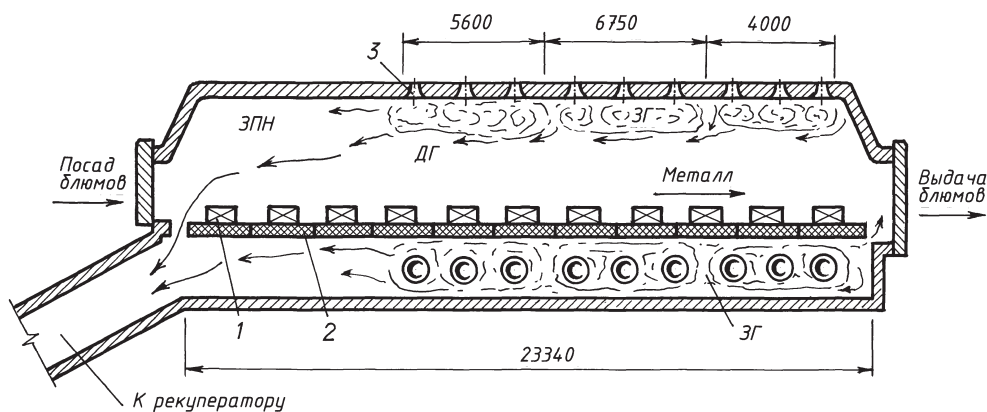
Схема нагревательной печи стана 850 РУП «БМЗ»: 1 – заготовка; 2 – шагающие балки; ЗПН – зона предварительного нагрева; ДГ – дымовые газы
